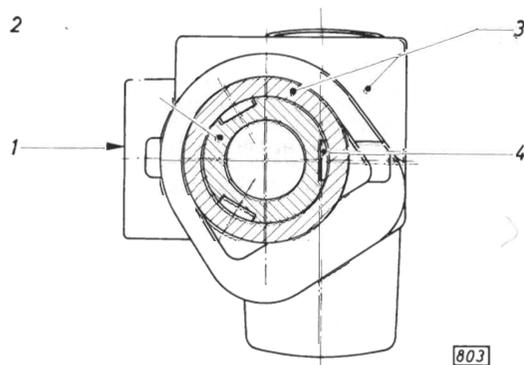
Lage der Sintermetallbuchse beim Eindrücken in Lenkgehäuse
